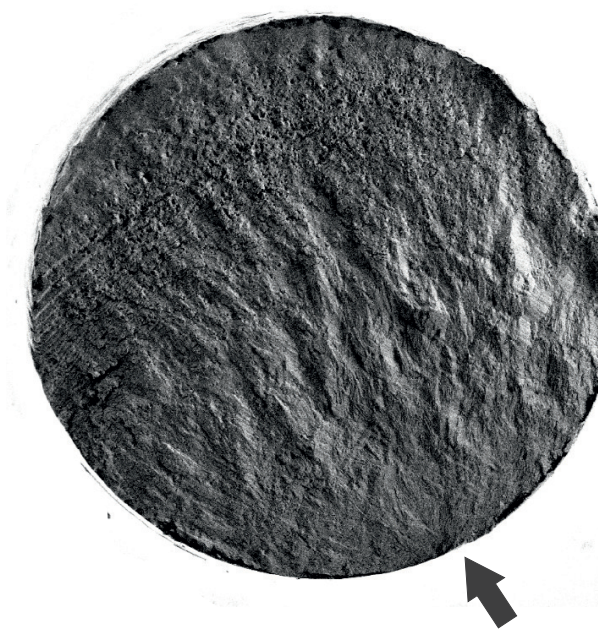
Vista de la superficie de fractura de la probeta R3A16 de entalla de radio 3.00 mm.
